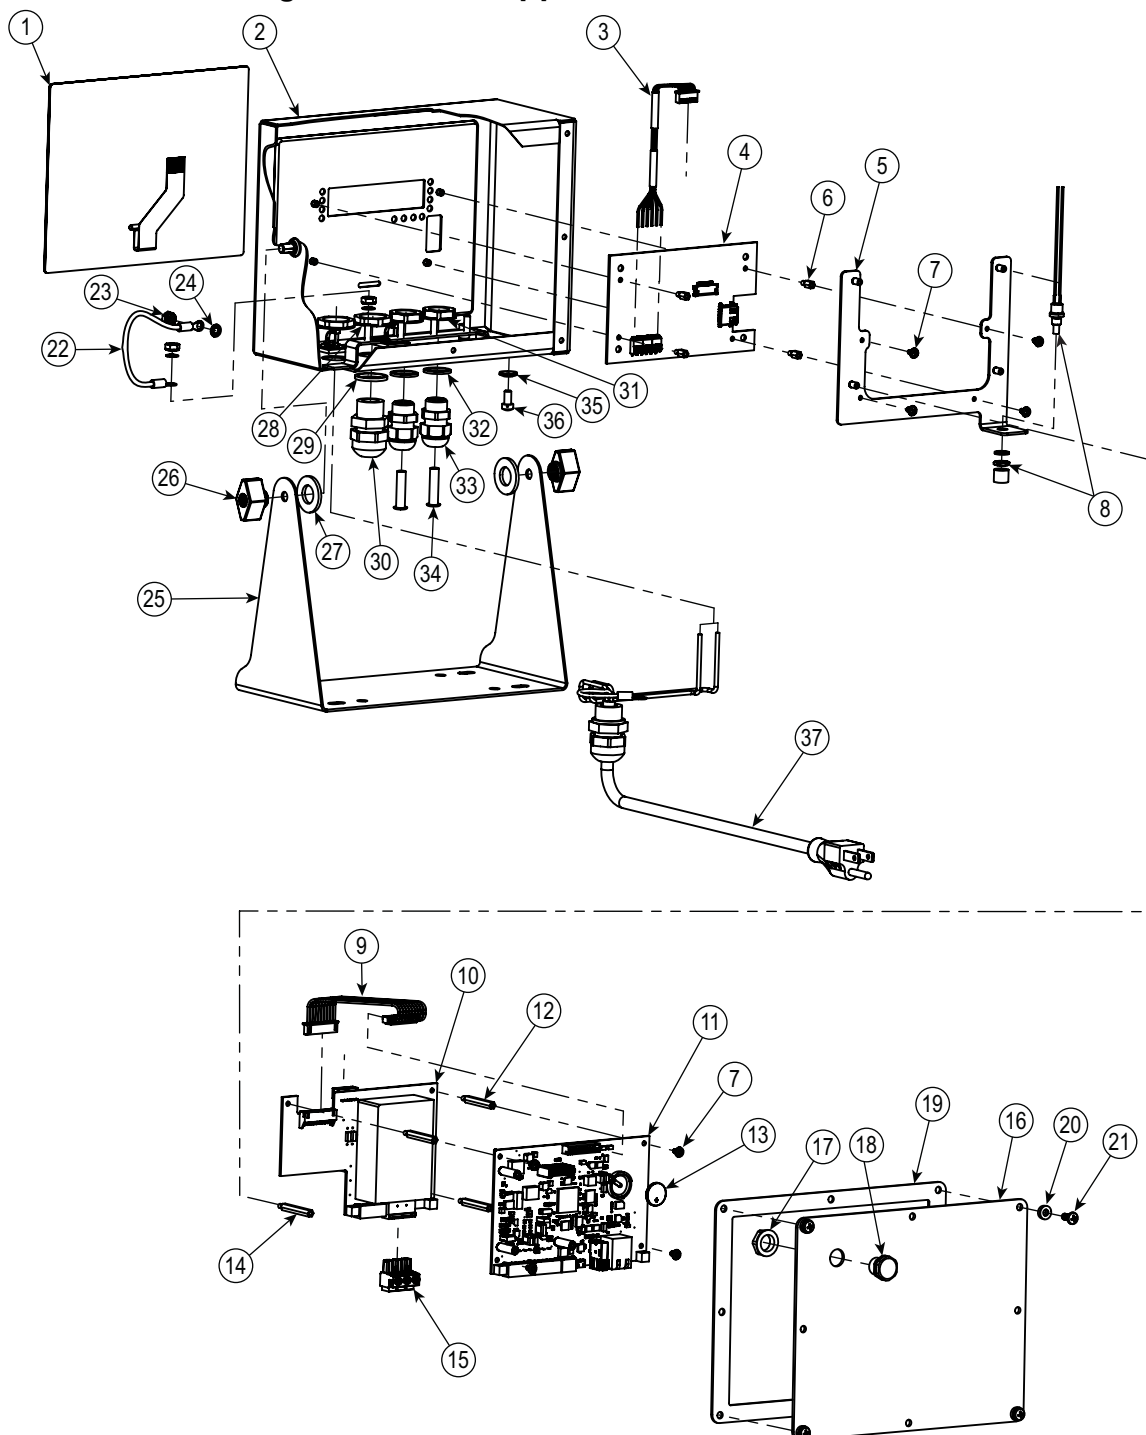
Illustration des pièces du modèle à support de fixation universel
